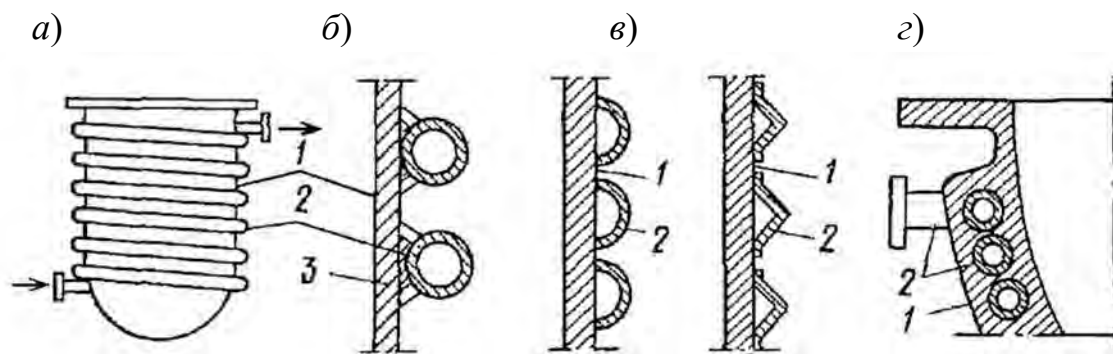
Аппараты с наружными змеевиками: а-в – с приваренными снаружи змеевиками различной формы; г – с залитыми при изготовлении в стенке змеевиками; 1 – корпуса аппаратов; 2 – змеевики; 3 – металлическая прокладка
